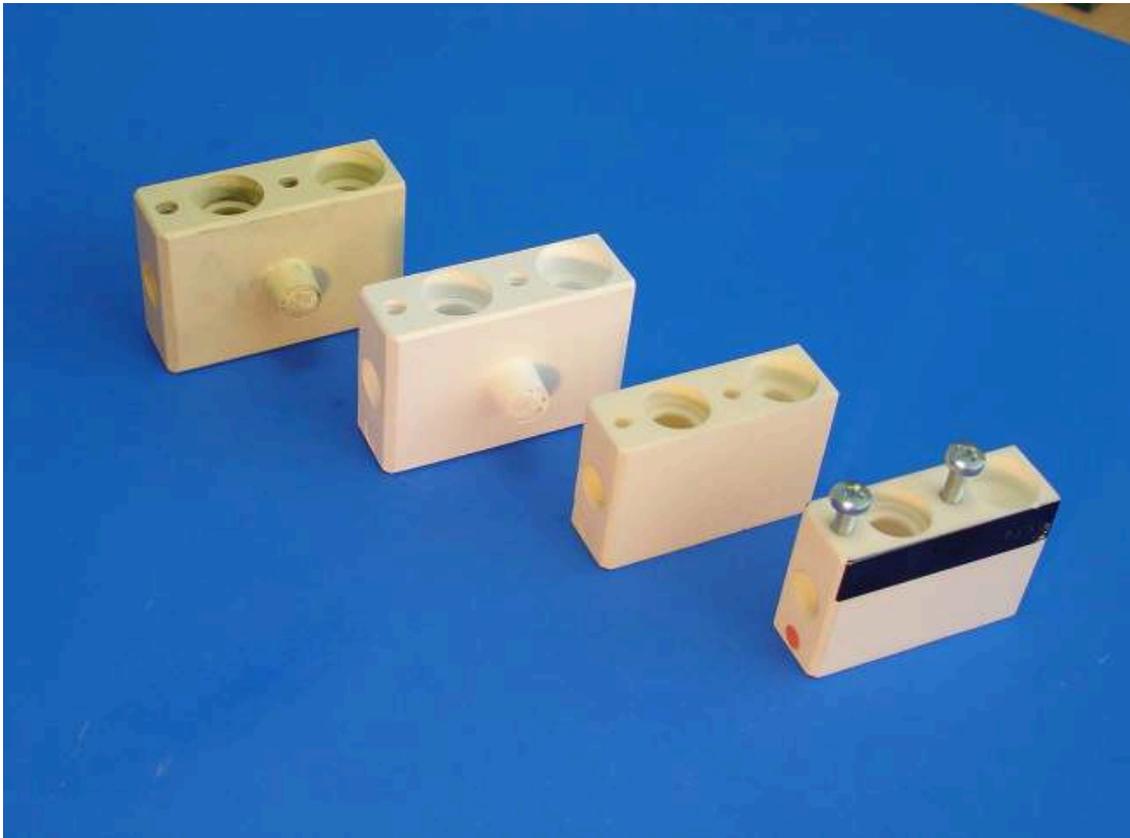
„Lampenfassung“ – Bearbeitungsstufen
